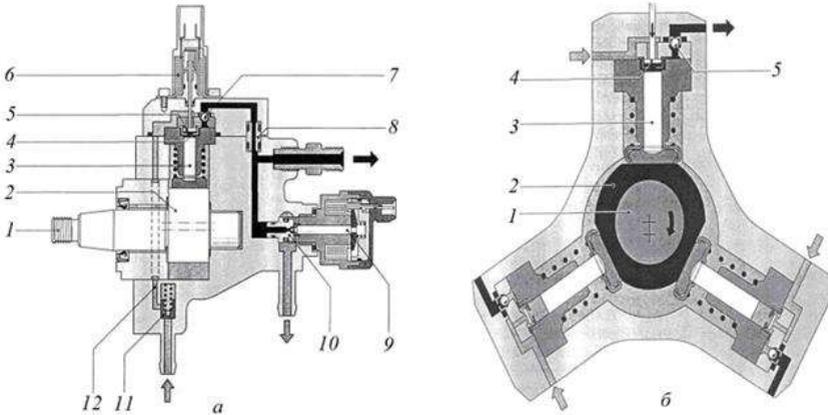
Конструкція ПНВТ системи CR:
